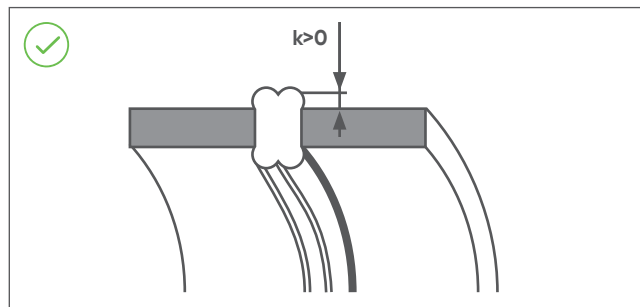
Schnittbild einer guten Schweißnaht
